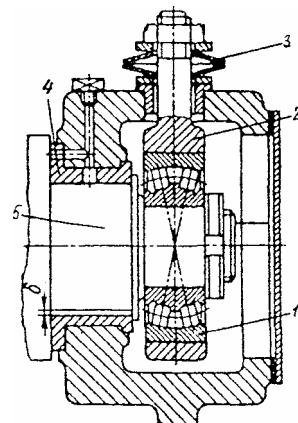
Подрессорный подцапфенник: 1-подшипник качения; 2 – обойма; 3 - тарельчатые пружины; 4 - подшипник скольжения; 5 - ступенчатая цапфа.
